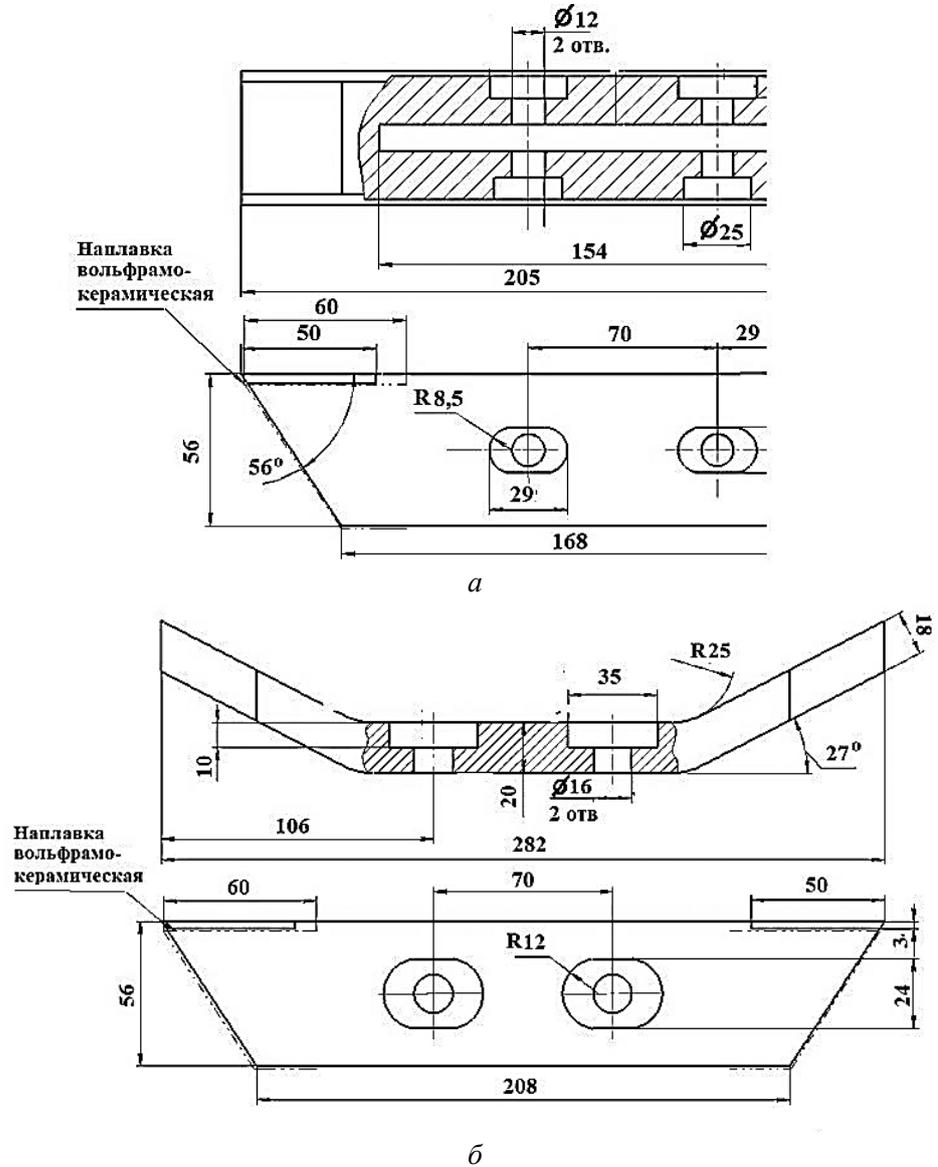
Резцы фрезы: а – прямой, б – отогнутый
